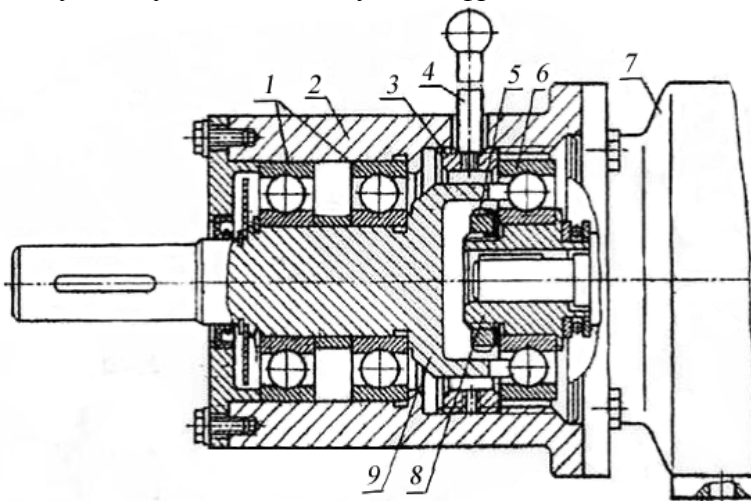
Мотор-редуктор из стандартных подшипников
